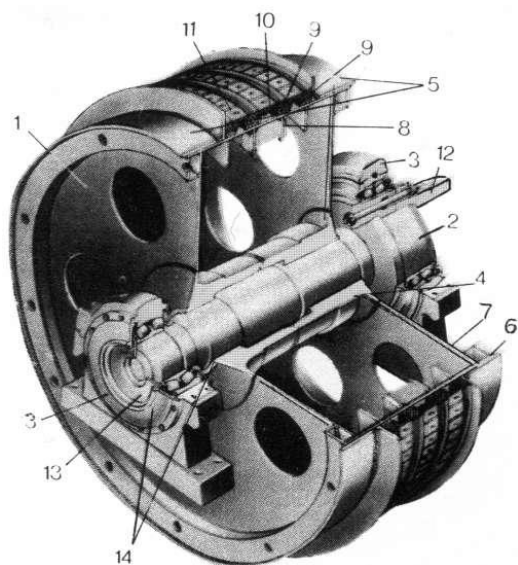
Зборка головного валу багатоканатної підйомної машини
